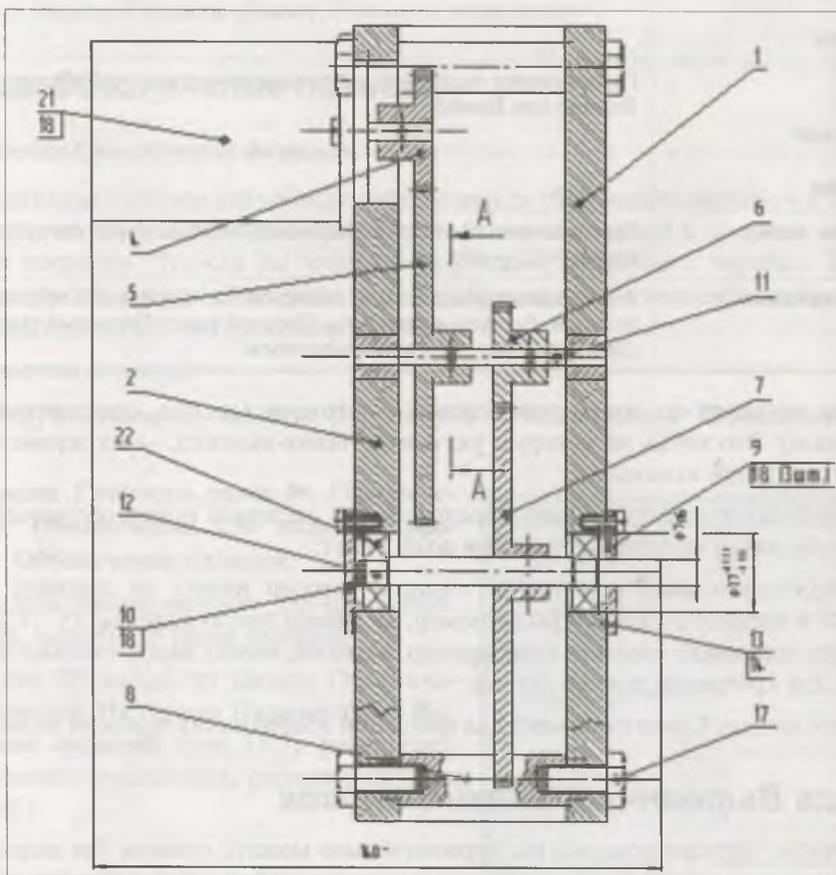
Сборочный чертеж Редуктор с проставленными позициями
